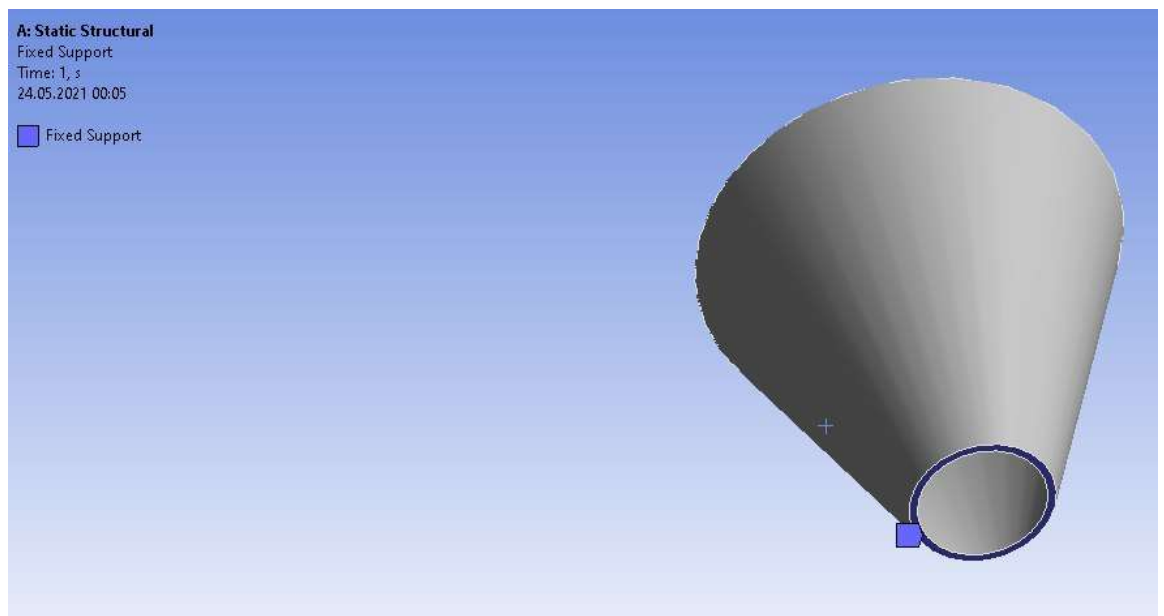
Початкова геометрія корпусу і закріплення бункеру.
